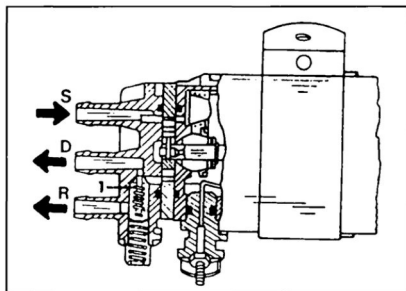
Разрез топливного насоса. 1 - клапан ограничения давления и обратный клапан, S-выпускной патрубок, D - выходящий патрубок, R - сливной патрубок.
